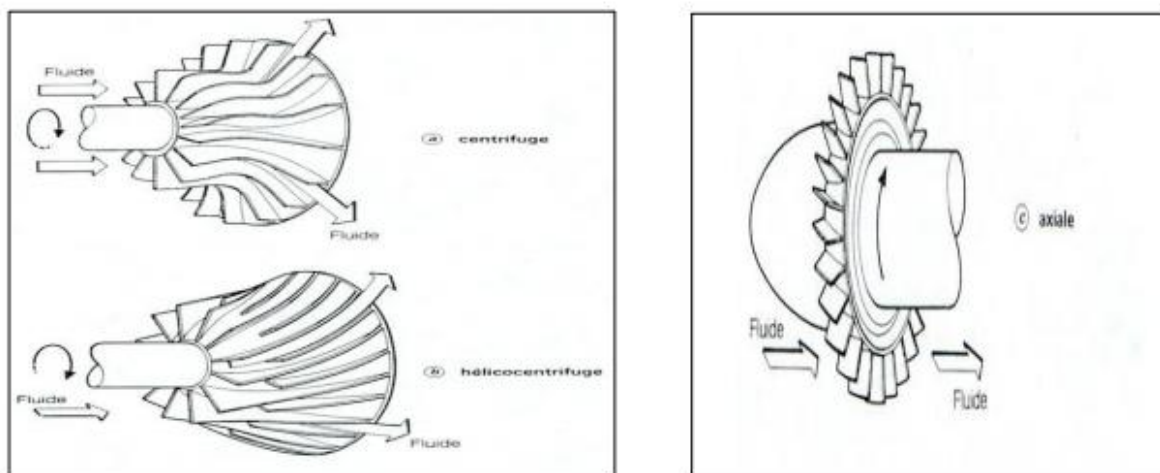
Roues mobiles de machines centrifuge, hélico centrifuge et axiale. [12]
